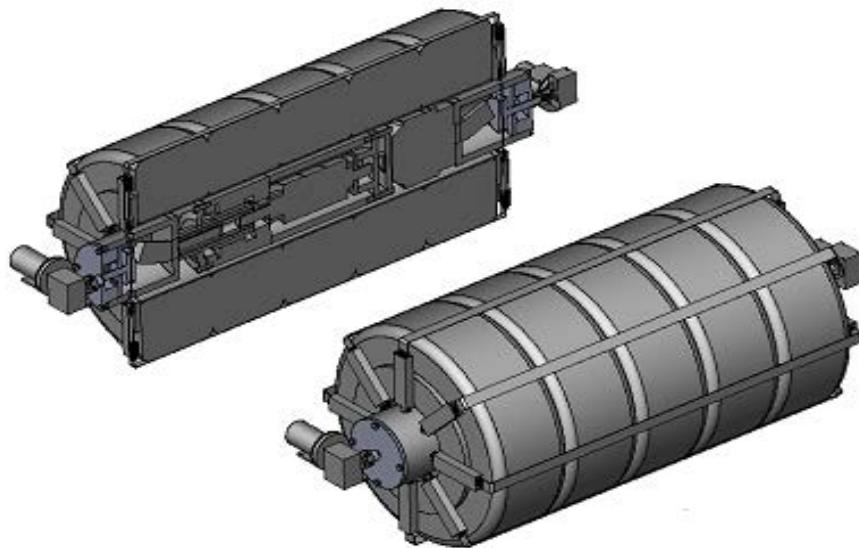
Вибрационный пневмошарнирный валец с металлическими бандажами
